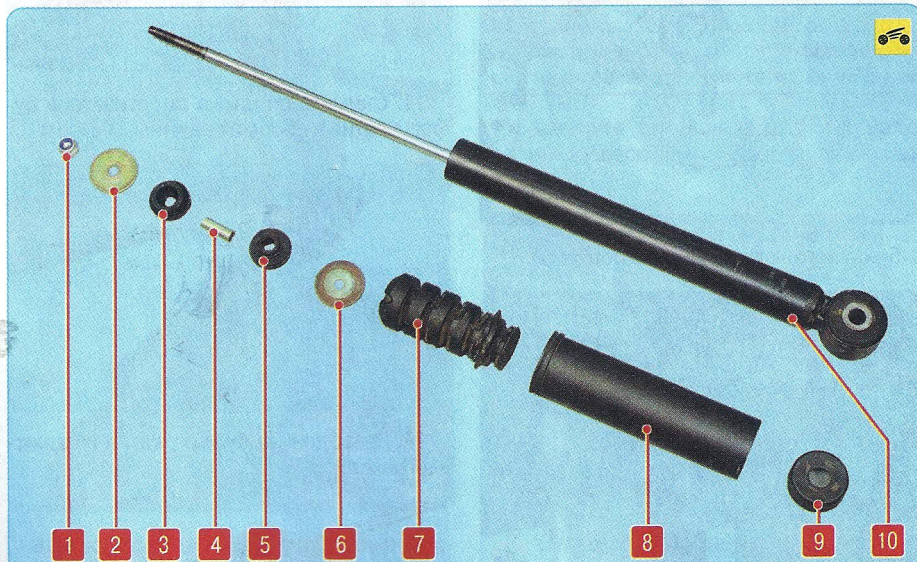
Детали амортизатора задней подвески: 1 – гайка крепления штока амортизатора; 2, 6 – шайбы; 3 – верхняя резиновая втулка; 4 – распорная втулка; 5 – нижняя резиновая втулка; 7 – буфер сжатия; 8 – защитный чехол; 9 – защитный колпачок; 10 – амортизатор
